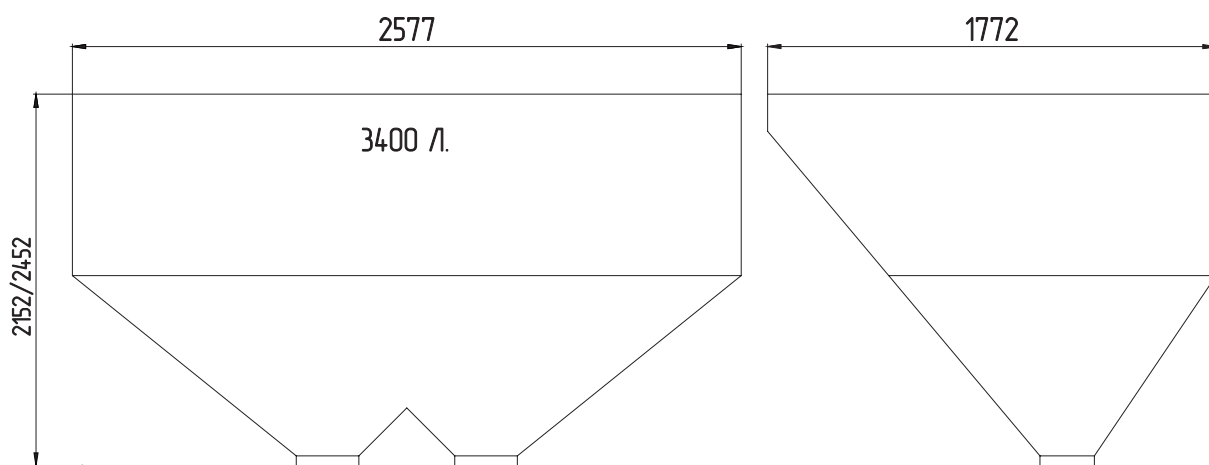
Габаритные размеры топливного бункера 3400 л 2 горла
